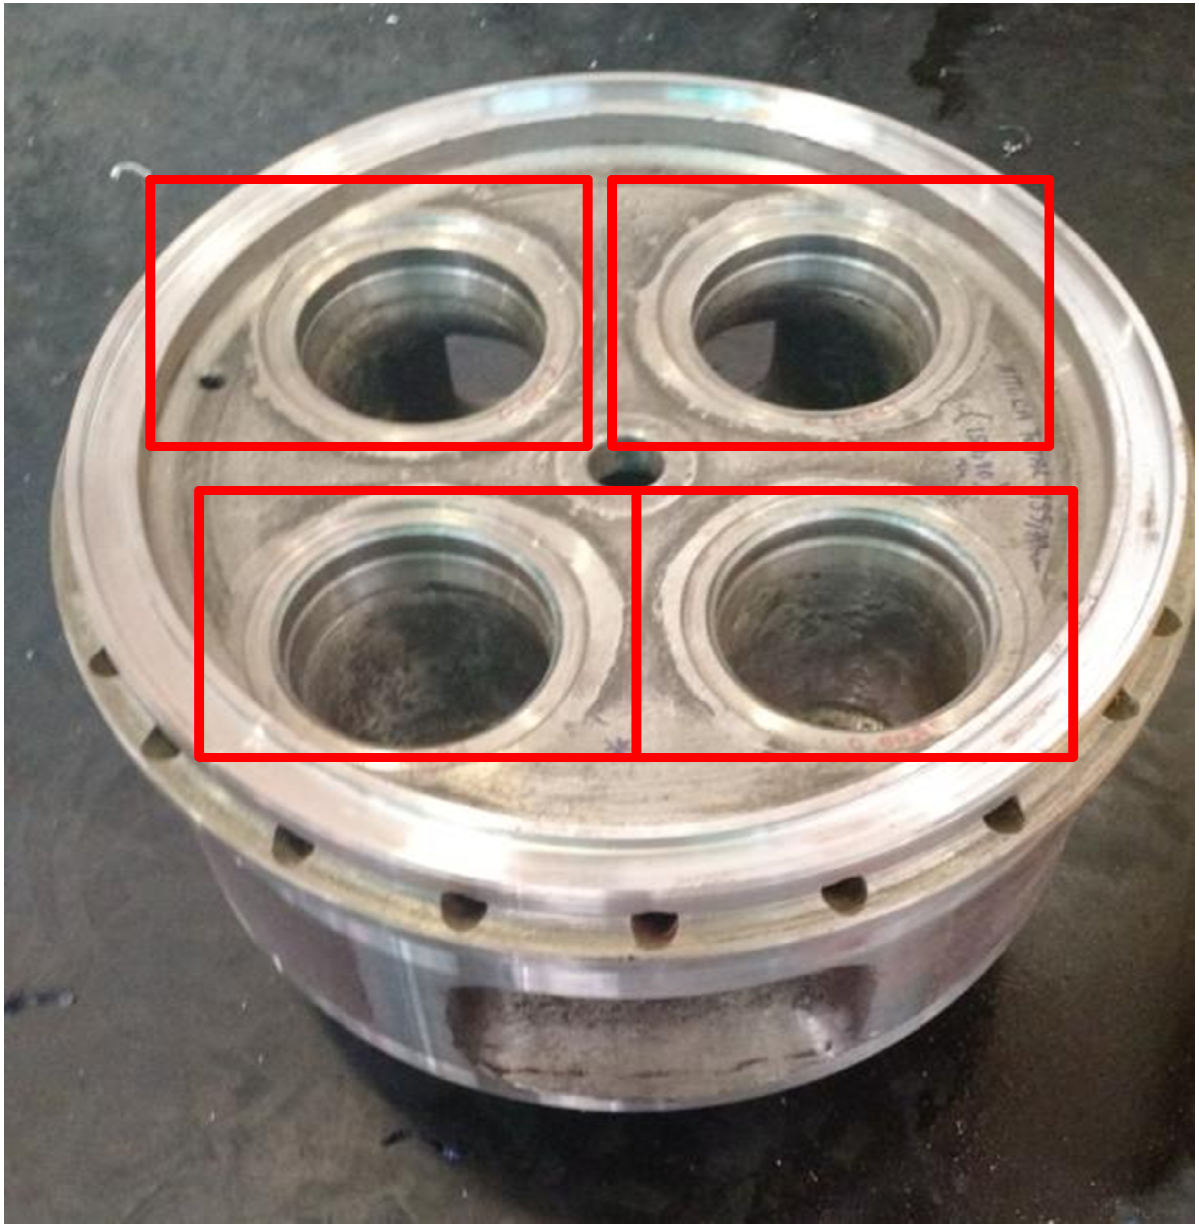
Vista superior de um cabeçote de motor 7FDL
